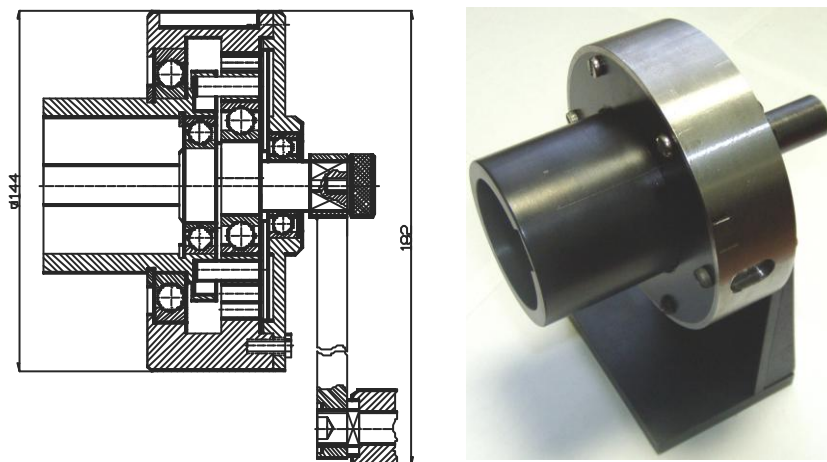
Малогабаритный редуктор для подъема крышки шахтной печи ($i = 32$)
